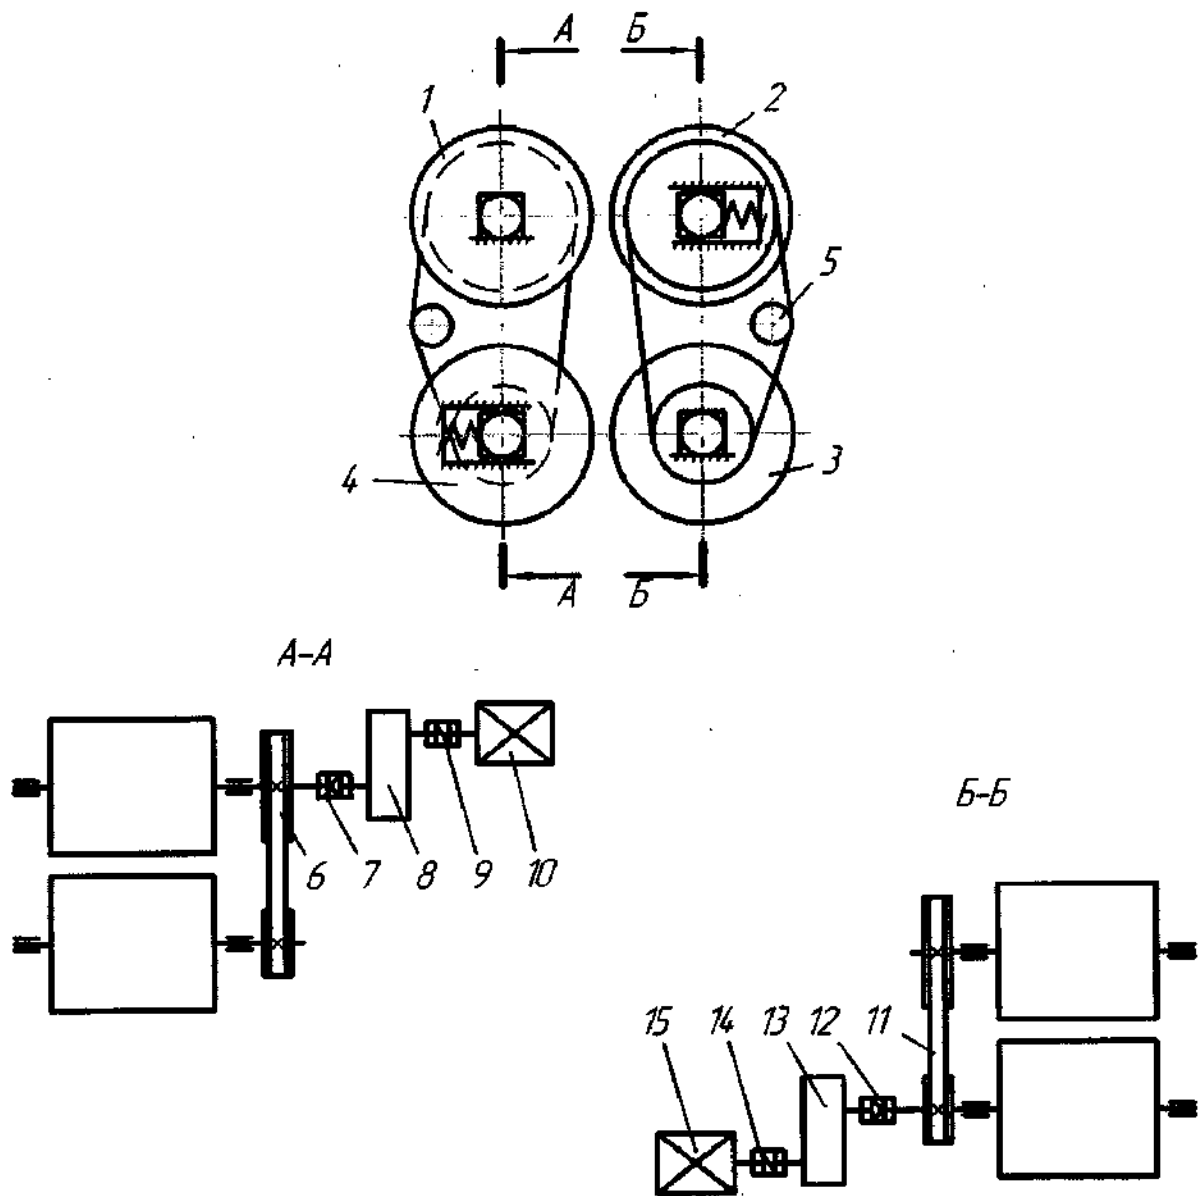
Загальний вид чотиривалкової дробарки Д4Г 900×700
